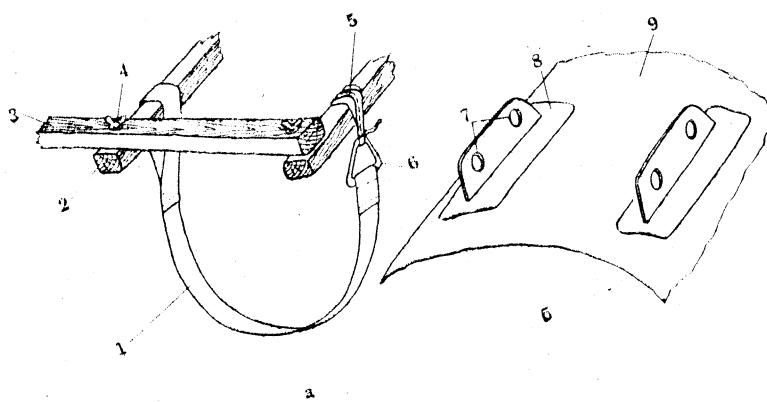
Способы крепления баллонов к платформе: а — с помощью ленты; б — с помощью накладок с люверсами; 1 — лента; 2 — продольный брус платформы; 3 — поперечная балка; 4 — болт с шайбами и барабашком; 5 — шнур; 6 — скоба из стальной проволоки; 7 — люверсы; 8 — накладка из прорезиненной ткани; 9 — поверхность баллона
